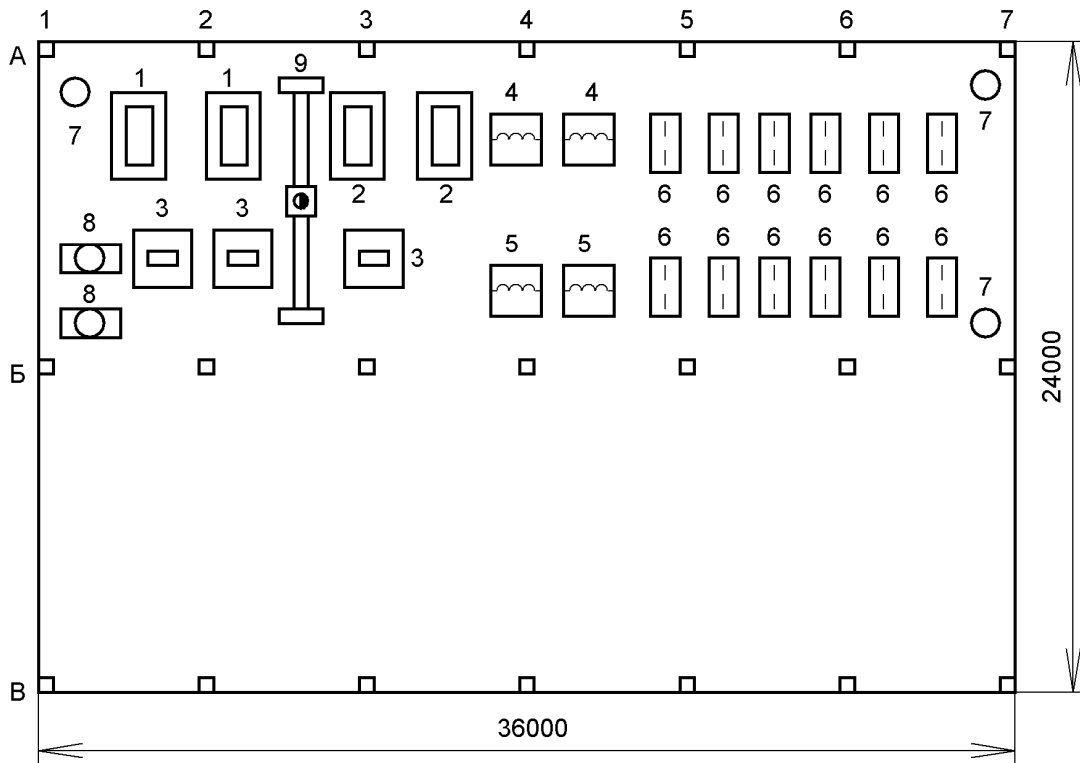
Схематичний план зварювально-термічної ділянки механічного цеху.
